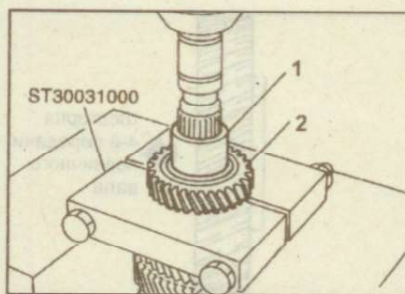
Выпрессовка втулки (1) шестерни 5-й передачи и шестерни 4-й передачи (2)
